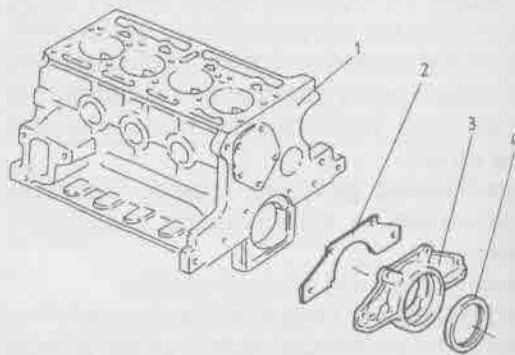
Demontaż pokrywy uszczelniającej wału korbowego od strony koła zamachowego (samochód z silnikiem 899)
